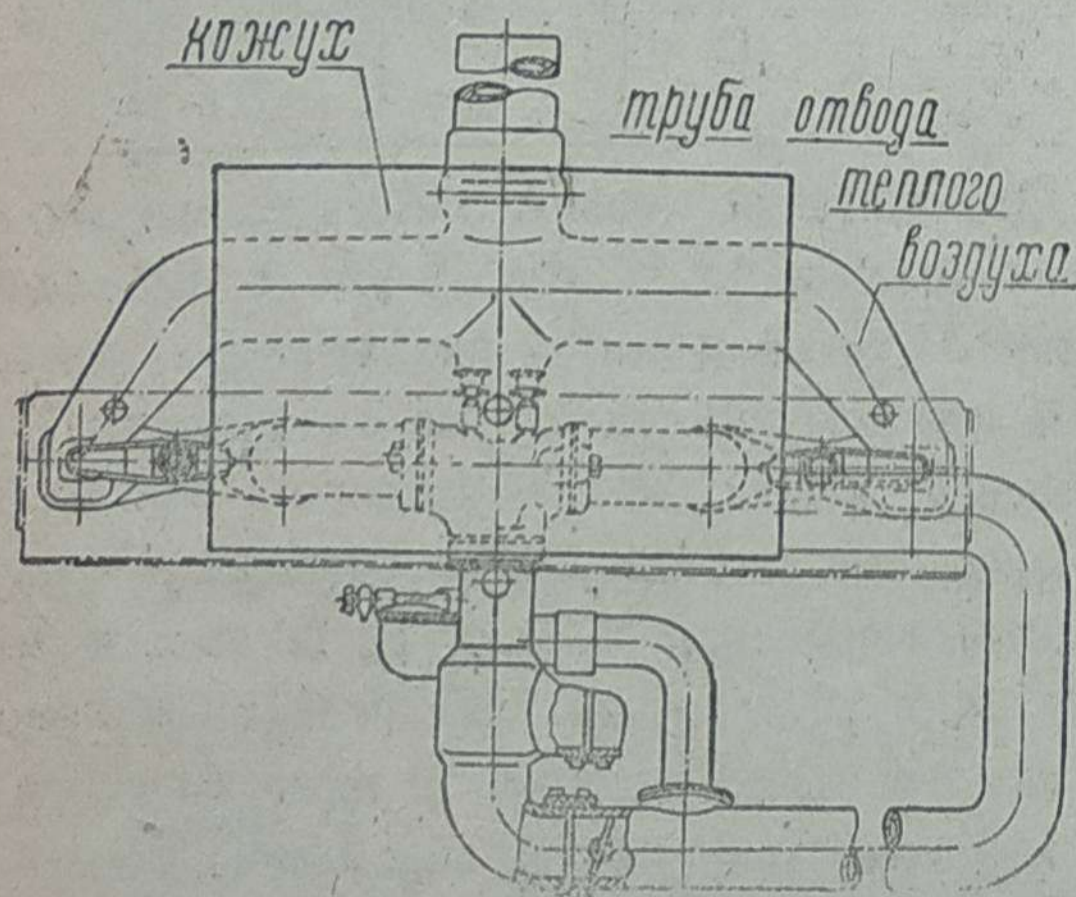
Схема установки обогревателя (кожуха) на двигатель трактора «ХТЗ-Т2Г».
